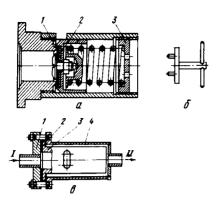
Предохранительный клапан компрессора П110 и приспособления для его регулировки:
